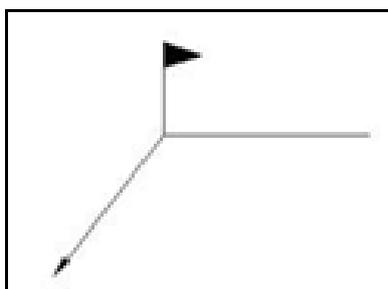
Indicación de soldadura realizada en la obra o en el campo.
